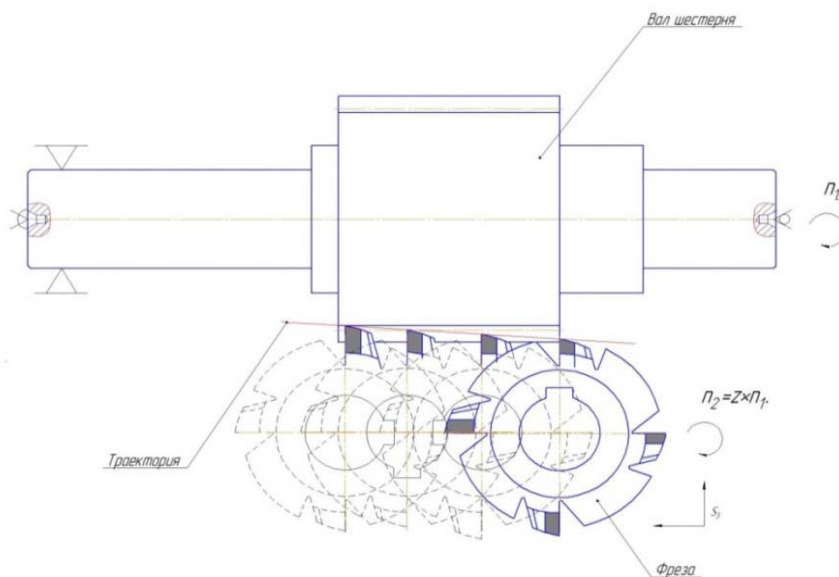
Схема нарезания зубьев на токарном станке с дисковой модульной фрезой
